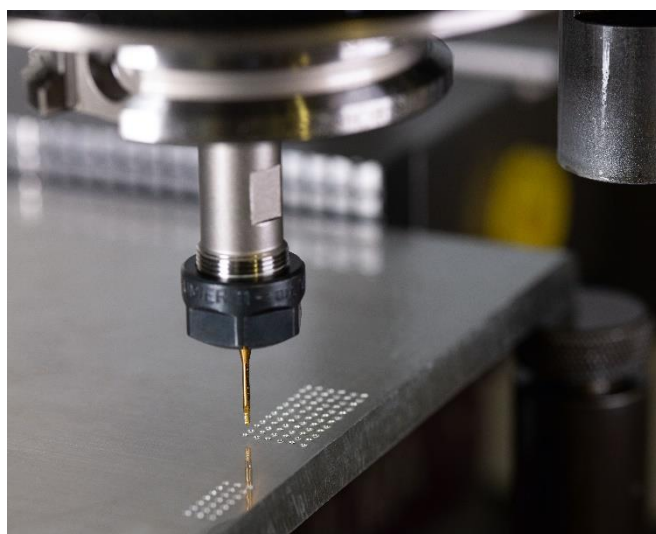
Der Punch Tap M1 im Einsatz in einer Aluminiumlegierung.
